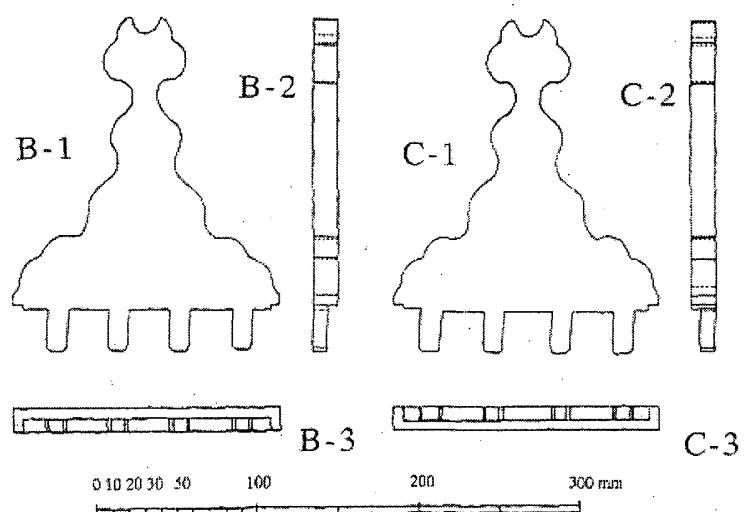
香月家旧蔵地球儀 支柱の平面及び断面図
